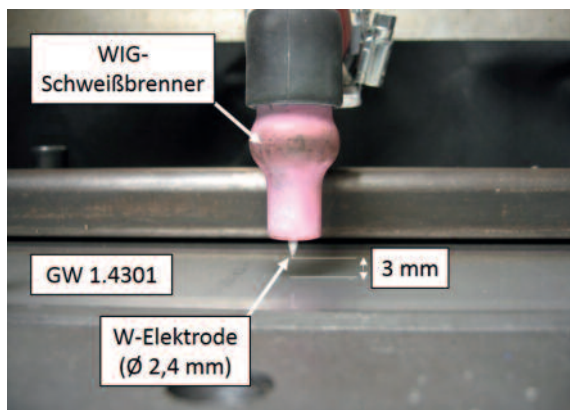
• Grundanordnung der WIG-Schweißversuche.
